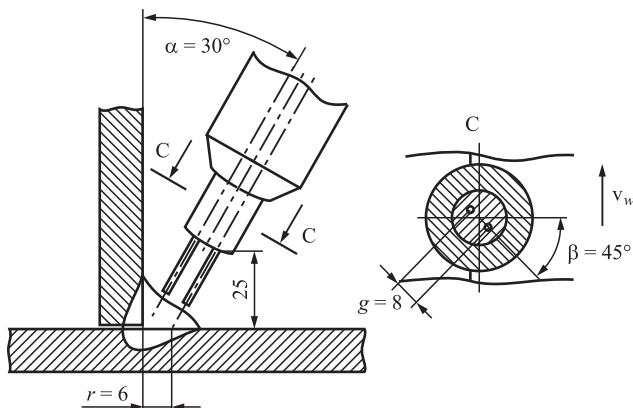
Схема расположения горелки относительно заготовок, поперечное сечение мундштука горелки и расположения сварочных проволок
